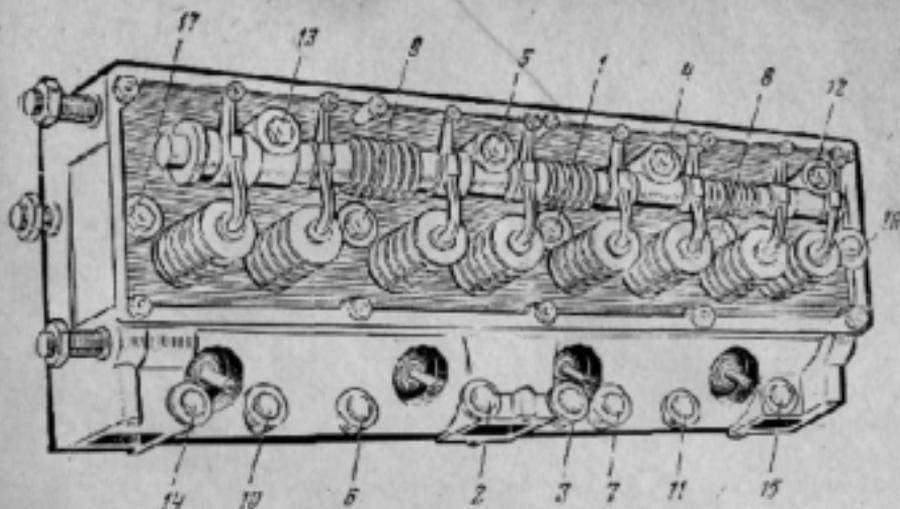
Порядок затягивания болтов крепления головки цилиндров
